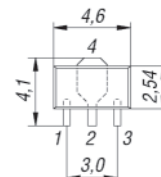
Pinbelegung und Abmessungen (SOT-89)
